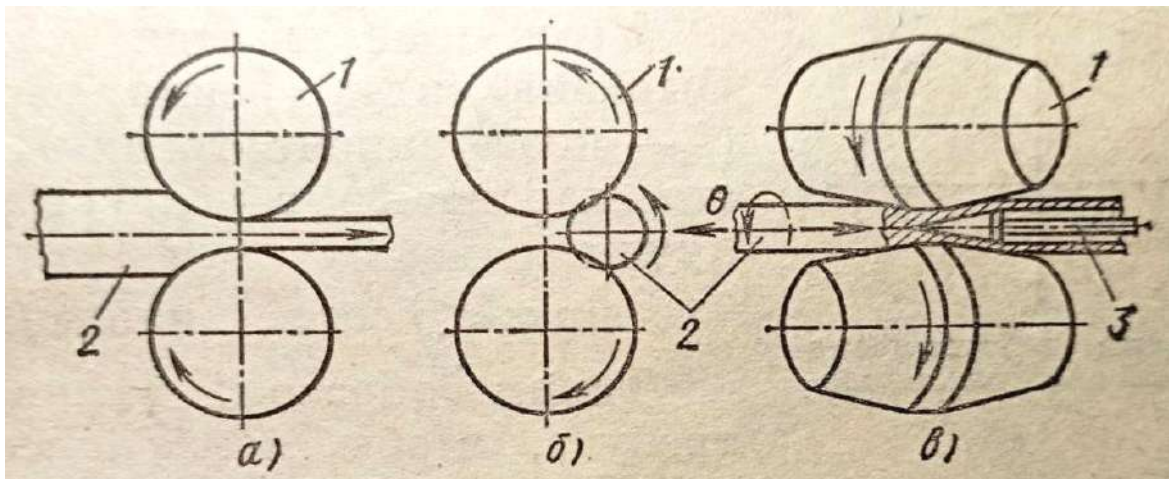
Основні види прокатки: а- подовжня; б – поперечна; в – поперечно-гвинтова ; 1 – валки; 2 – заготовка ; 3 - оправка
